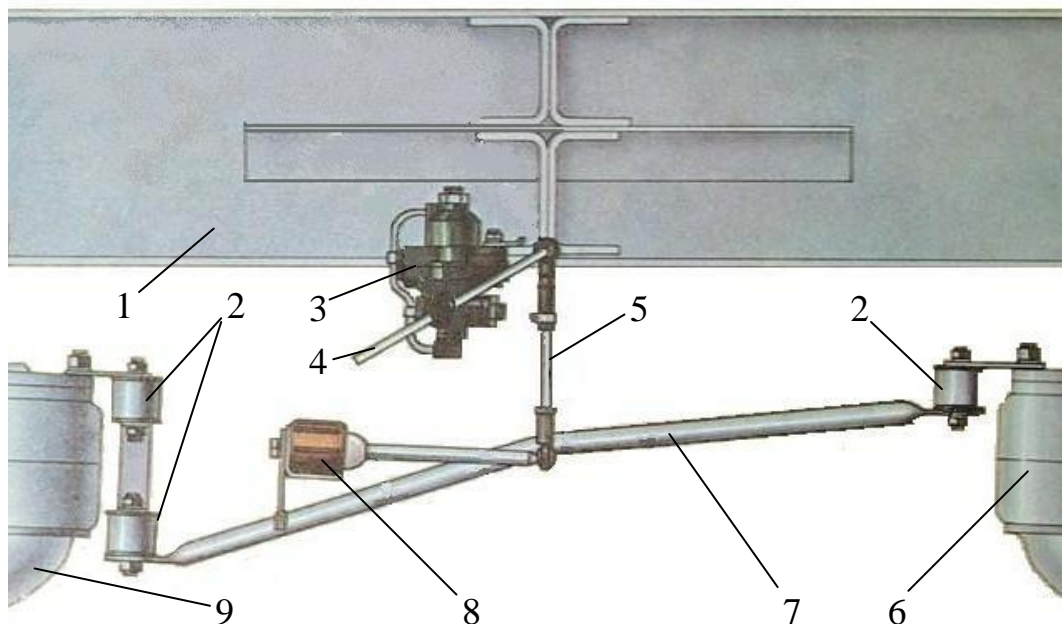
Установка автоматического регулятора тормозных сил тормозного привода грузового автомобиля-тягача КАМАЗ-5350: 1 – рама автомобиля; 2 – компенсаторы перемещения; 3 – регулятор тормозных сил; 4 – рычаг регулятора; 5 – тяга; 6 – балка заднего моста; 7 – соединительная штанга; 8 – упругий элемент; 9 – балка среднего моста
